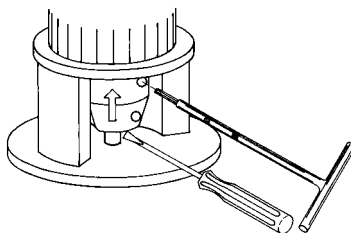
Dvíhanie spojky a hriadeľa čerpadla
